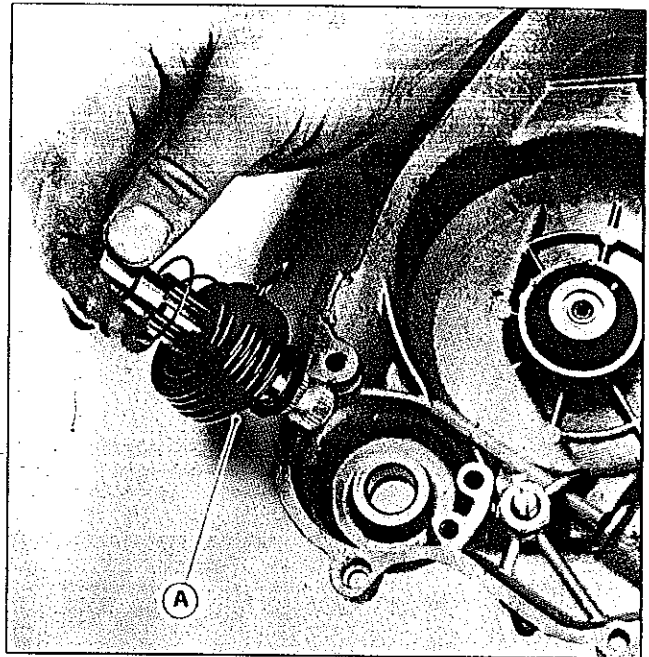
A. EIXO PEDAL DE ARRANQUE
